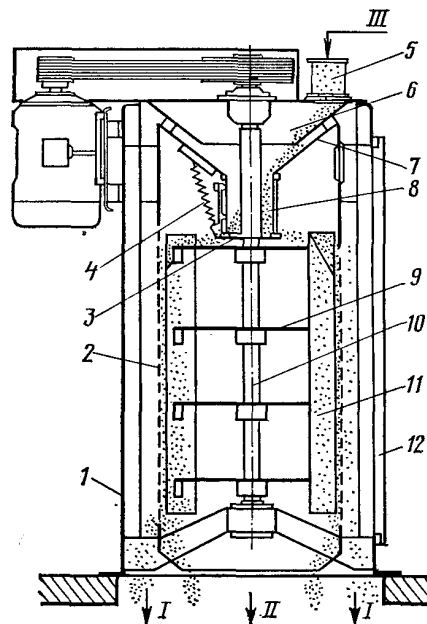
Вертикальна оббивна машина: 1 – корпус; 2 – сітчастий циліндр; 3 – диск; 4 – пружина; 5 – прийомний патрубок; 6 – завантажувальна лійка; 7 – нижній конус; 8 – живильний пристрій; 9 – розетка; 10 – ротор; 11 – бич; 12 – двері; I – відходи; II – очищене зерно; III – надходження зерна
